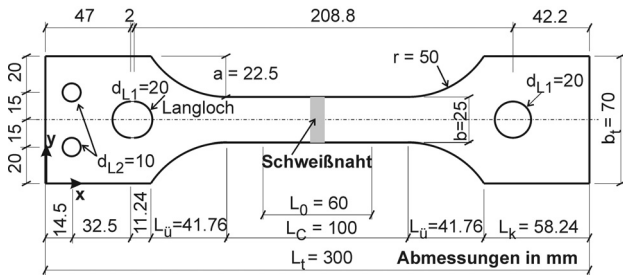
Geometrie der geschweißten Flachzugprobe
